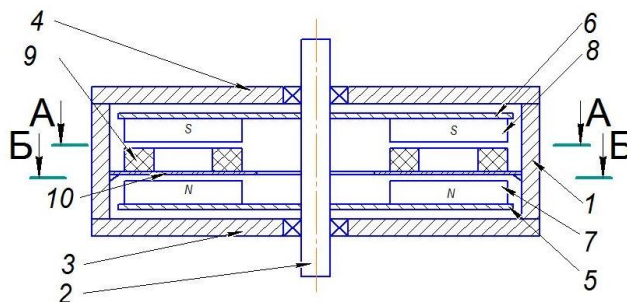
Маломощный ВЭГ с двухдисковым ротором: (пат. № 116482) 1 – цилиндрический корпус; 2 – вал; 3, 4 – подшипниковые щиты; 5, 6 – двухдисковый ротор; 7, 8 – неодимовые магниты; 9 – пустотелые катушки; 10 – бакелитовый статорный диск [2].
